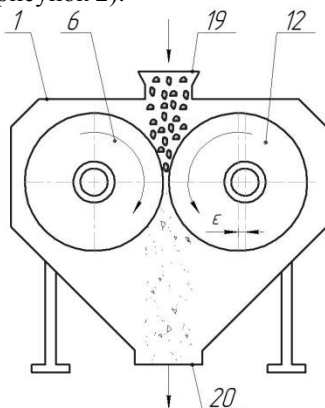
Схема вибровалкового измельчителя (вид сбоку)
